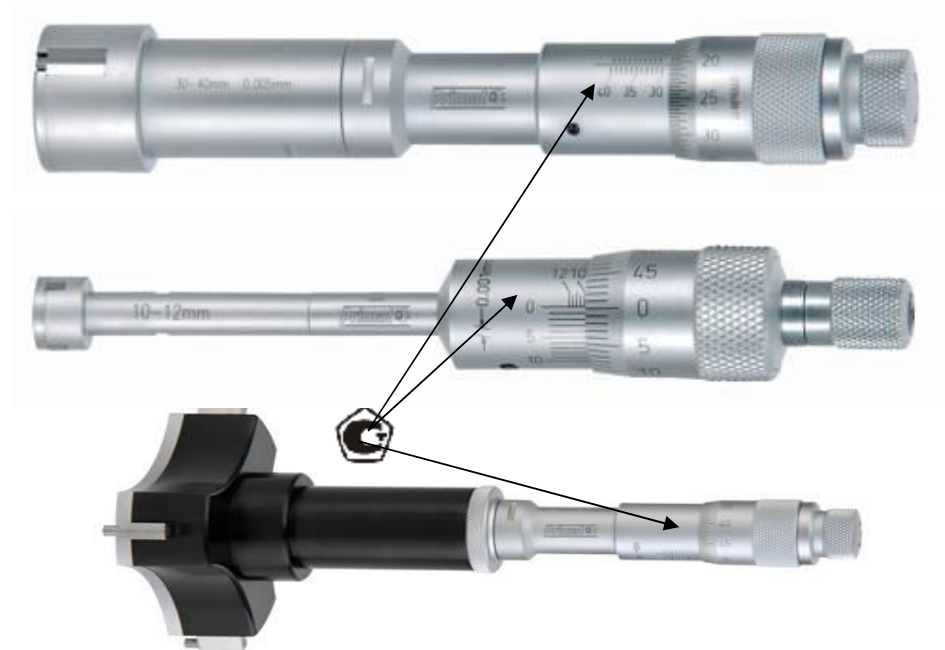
Общий вид нутромера микрометрического трехточечного Primat и место нанесения знаков утверждения типа.
